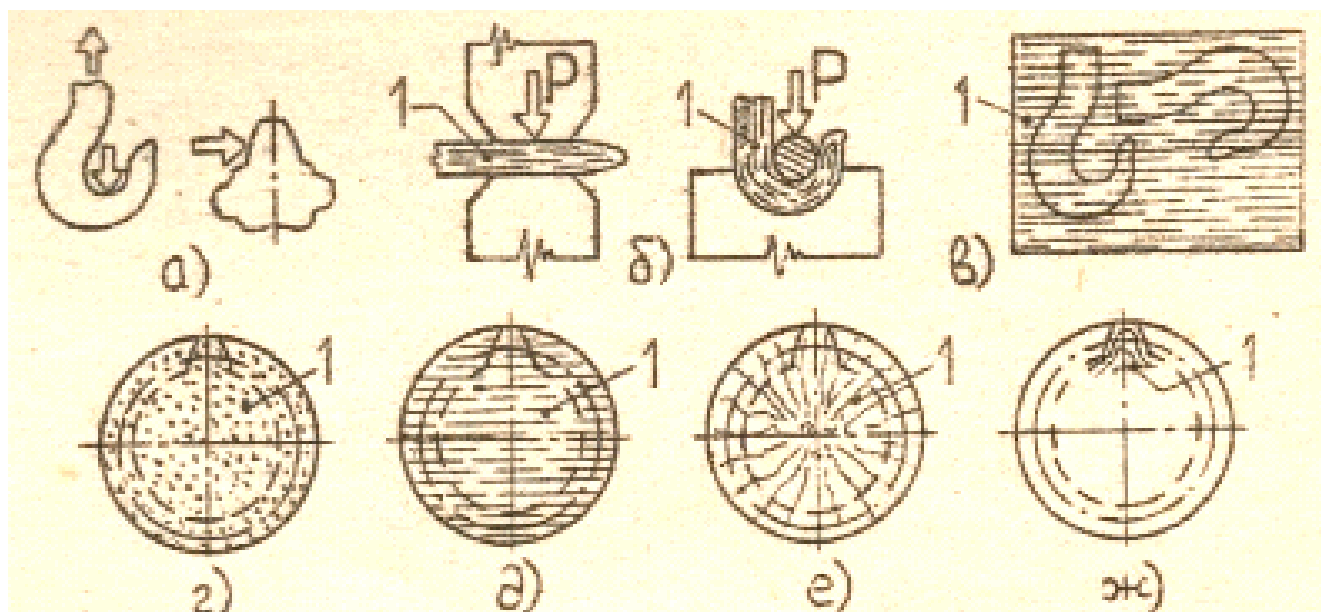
Варианты технологии получения заготовок для грузового крюка и зубчатого колеса: а — схема действия сил на крюк и зубья колеса при эксплуатации; б — ковка (протяжка и гибка); в — вырезка из катаного листа; г — катаный пруток; д — ковка катаного прутка плашмя; е — ковка катаного прутка в торец; ж — горячая накатка зубьев; 1 — волокна макроструктуры
